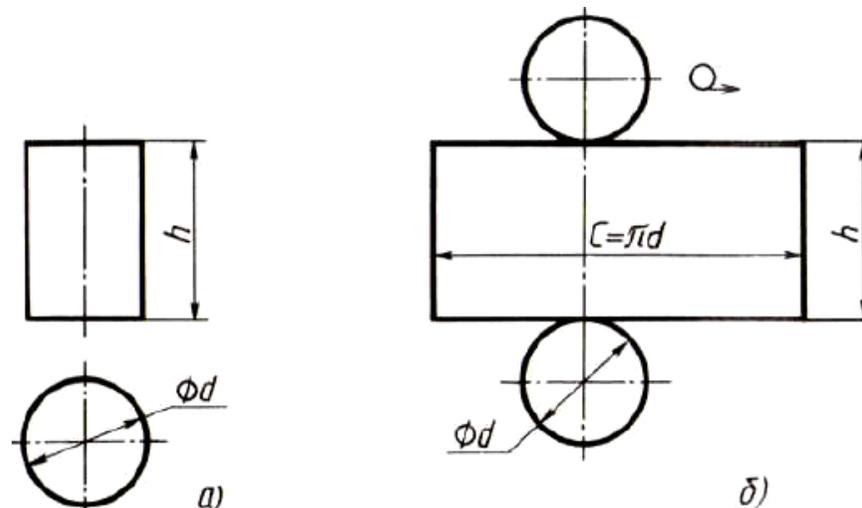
Построение чертежа развертки поверхностей цилиндра:
